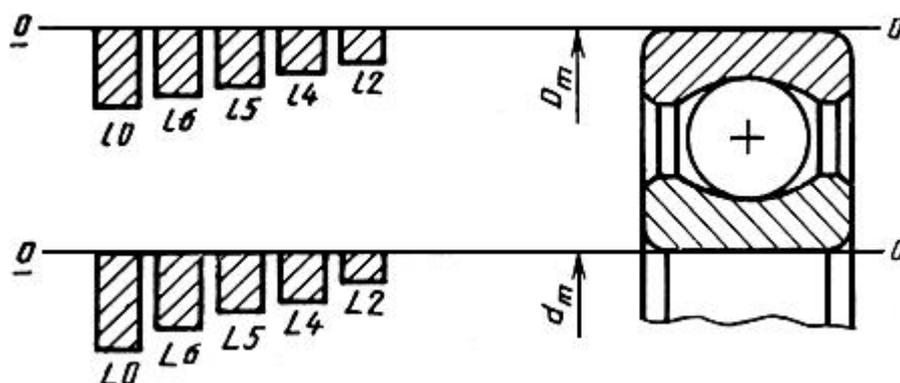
Схема расположения полей допусков на средний наружный диаметр и диаметр отверстия подшипников по классам точности
